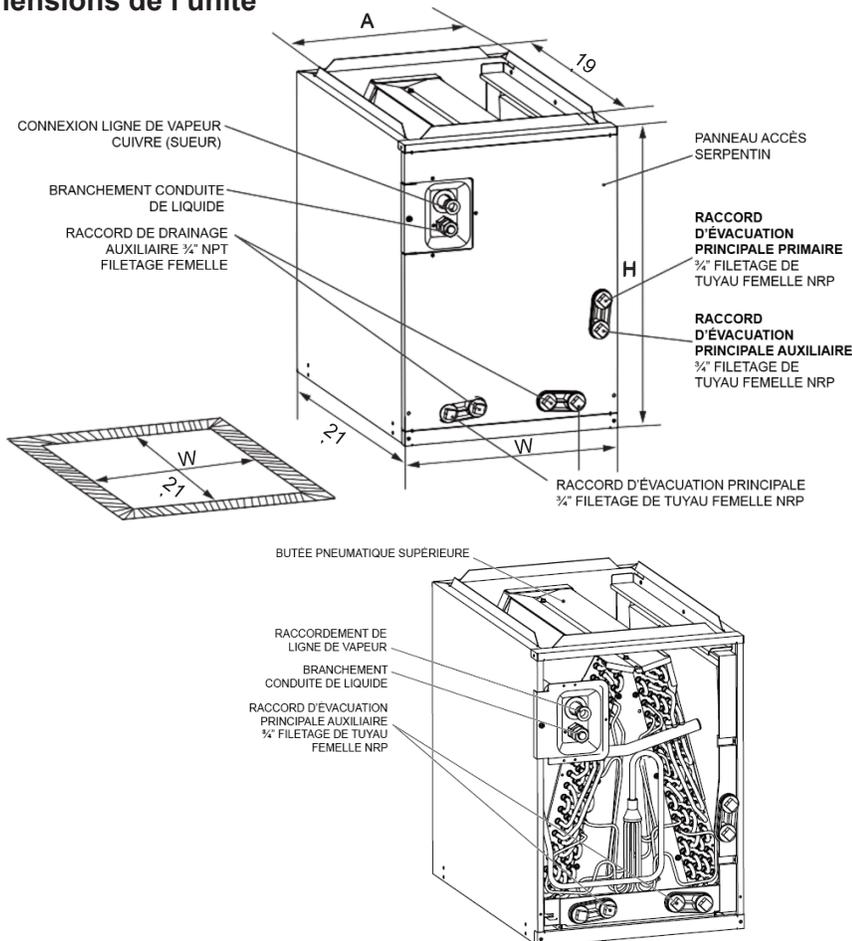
DIMENSIONS DU BOÎTIER ET EMPLACEMENT DES COMPOSANTS
